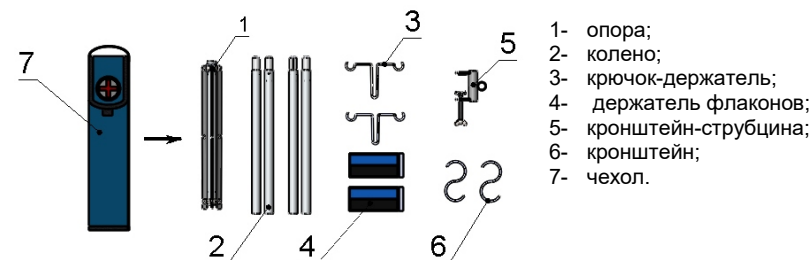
Устройство штатива разборного для инфузий ШР-«Медплант».
